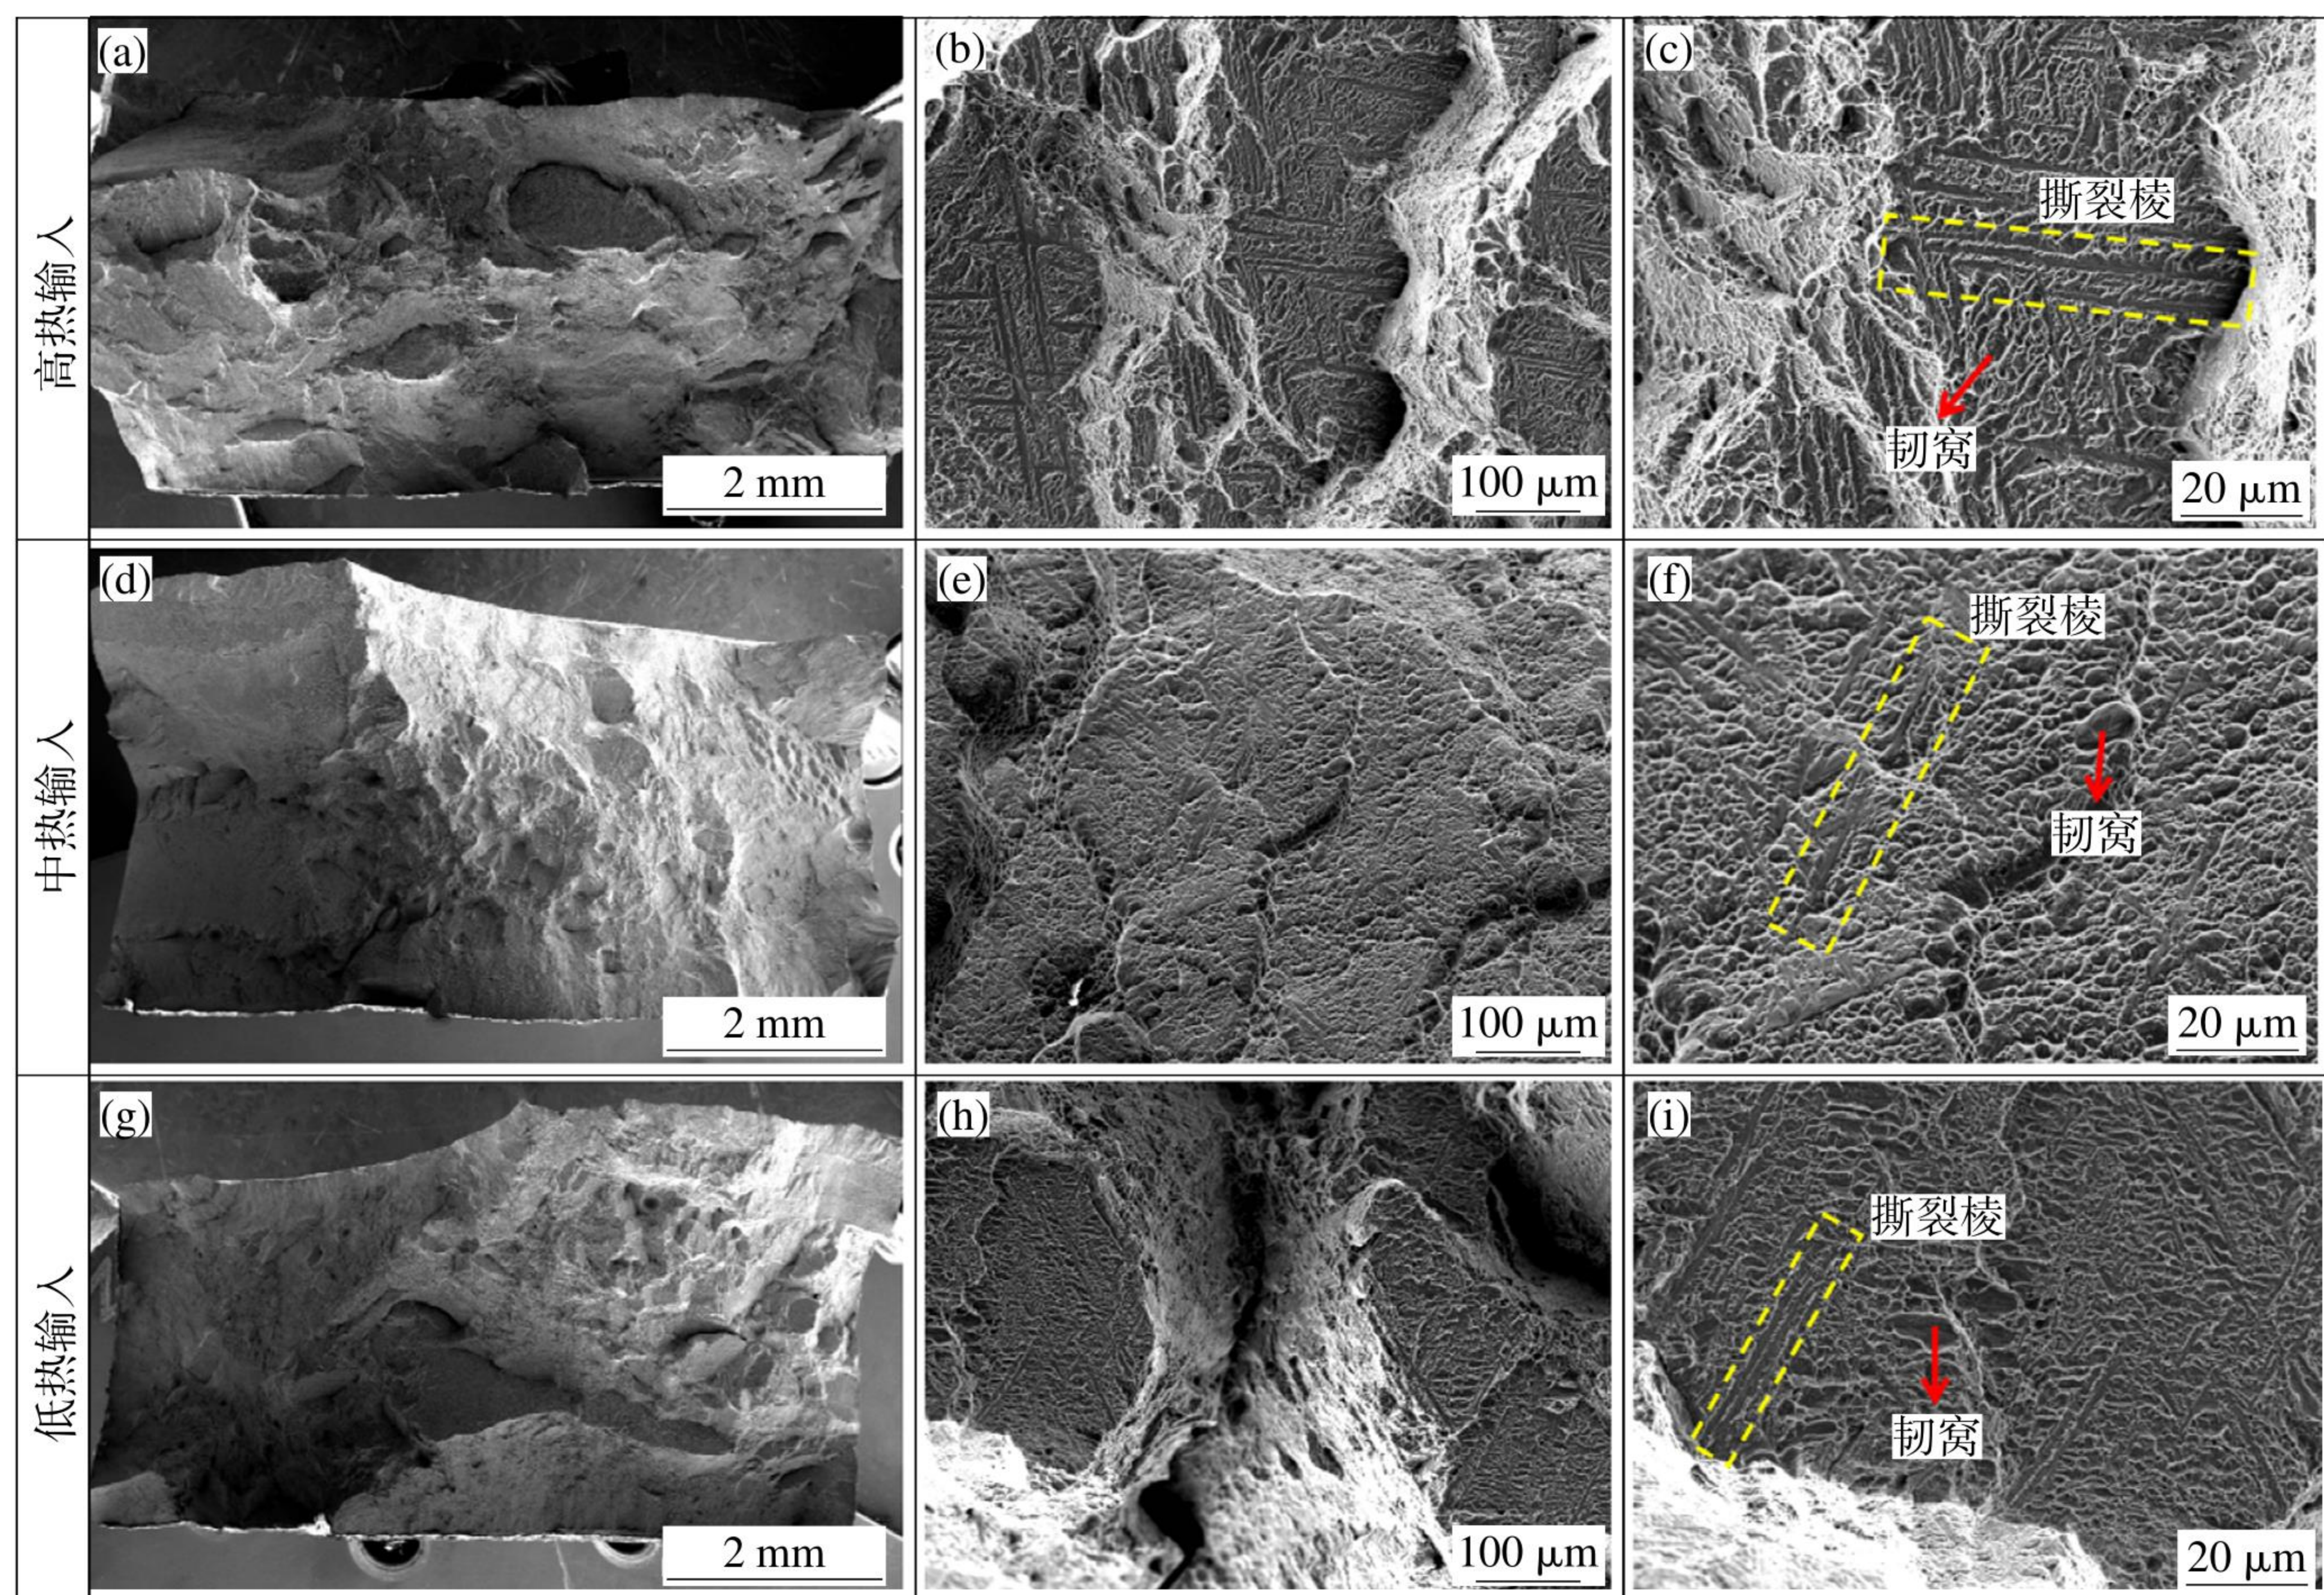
不同焊接热输入条件下拉伸试样的断口形貌
